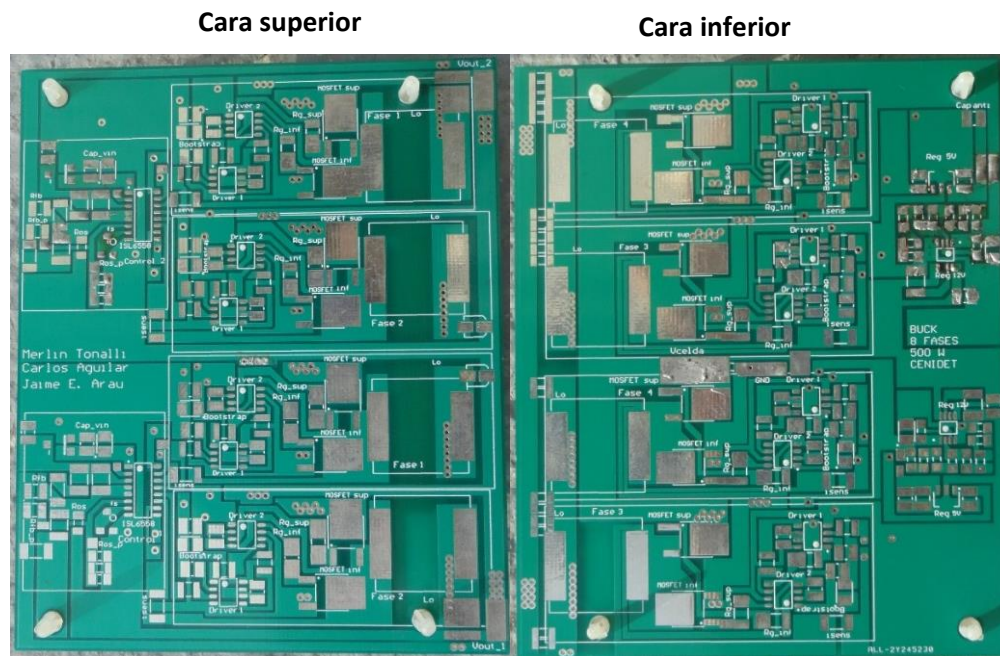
Tarjeta electrónica fabricada por la empresa ALL PCB.
